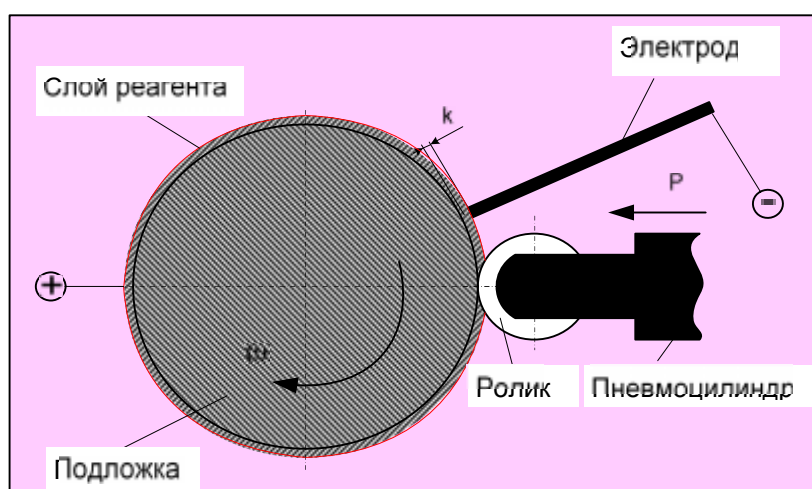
Схема процесса нанесения покрытий на деталях типа «вал»
